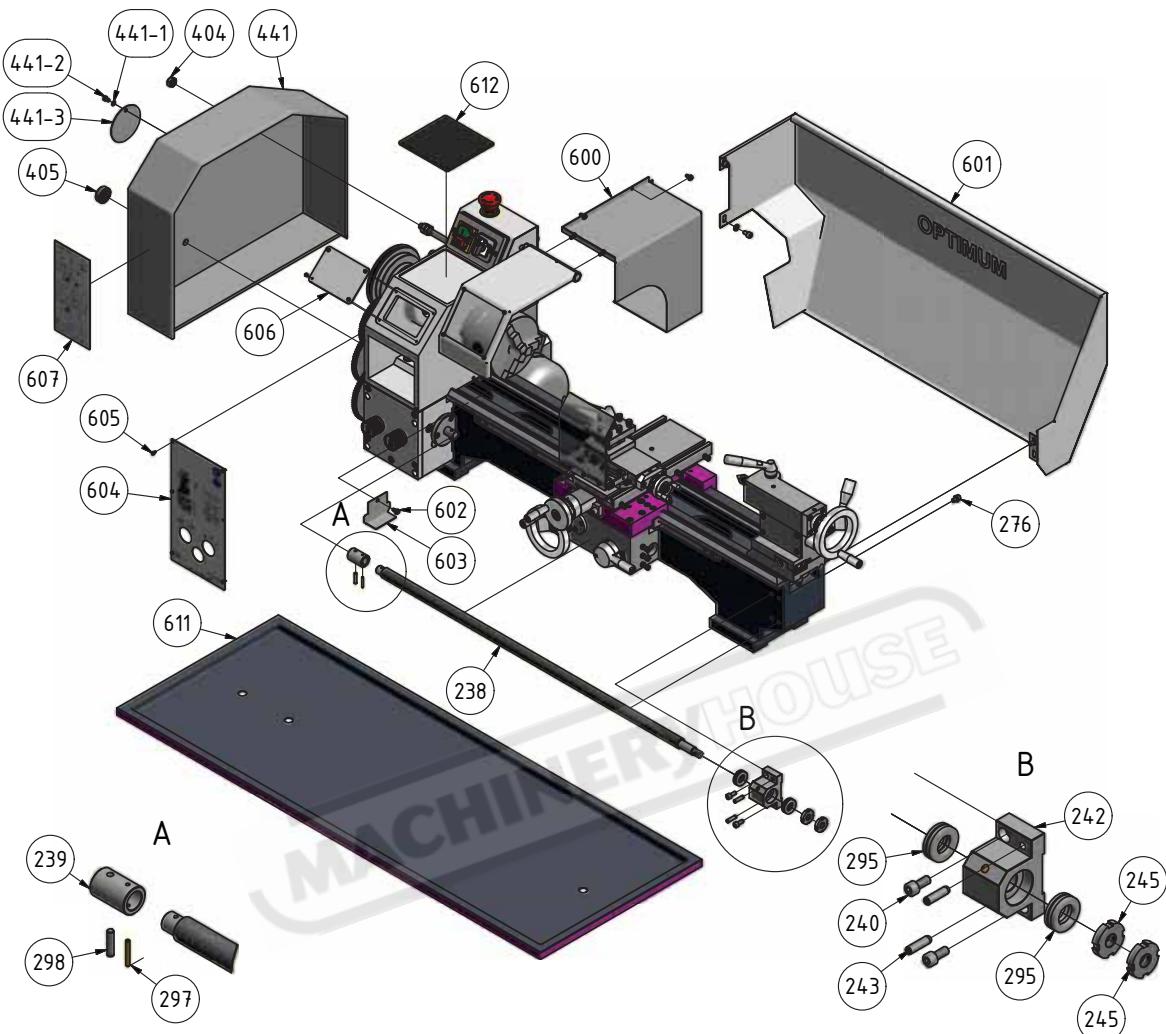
Maschinenbett - Machine bed TU 2506
